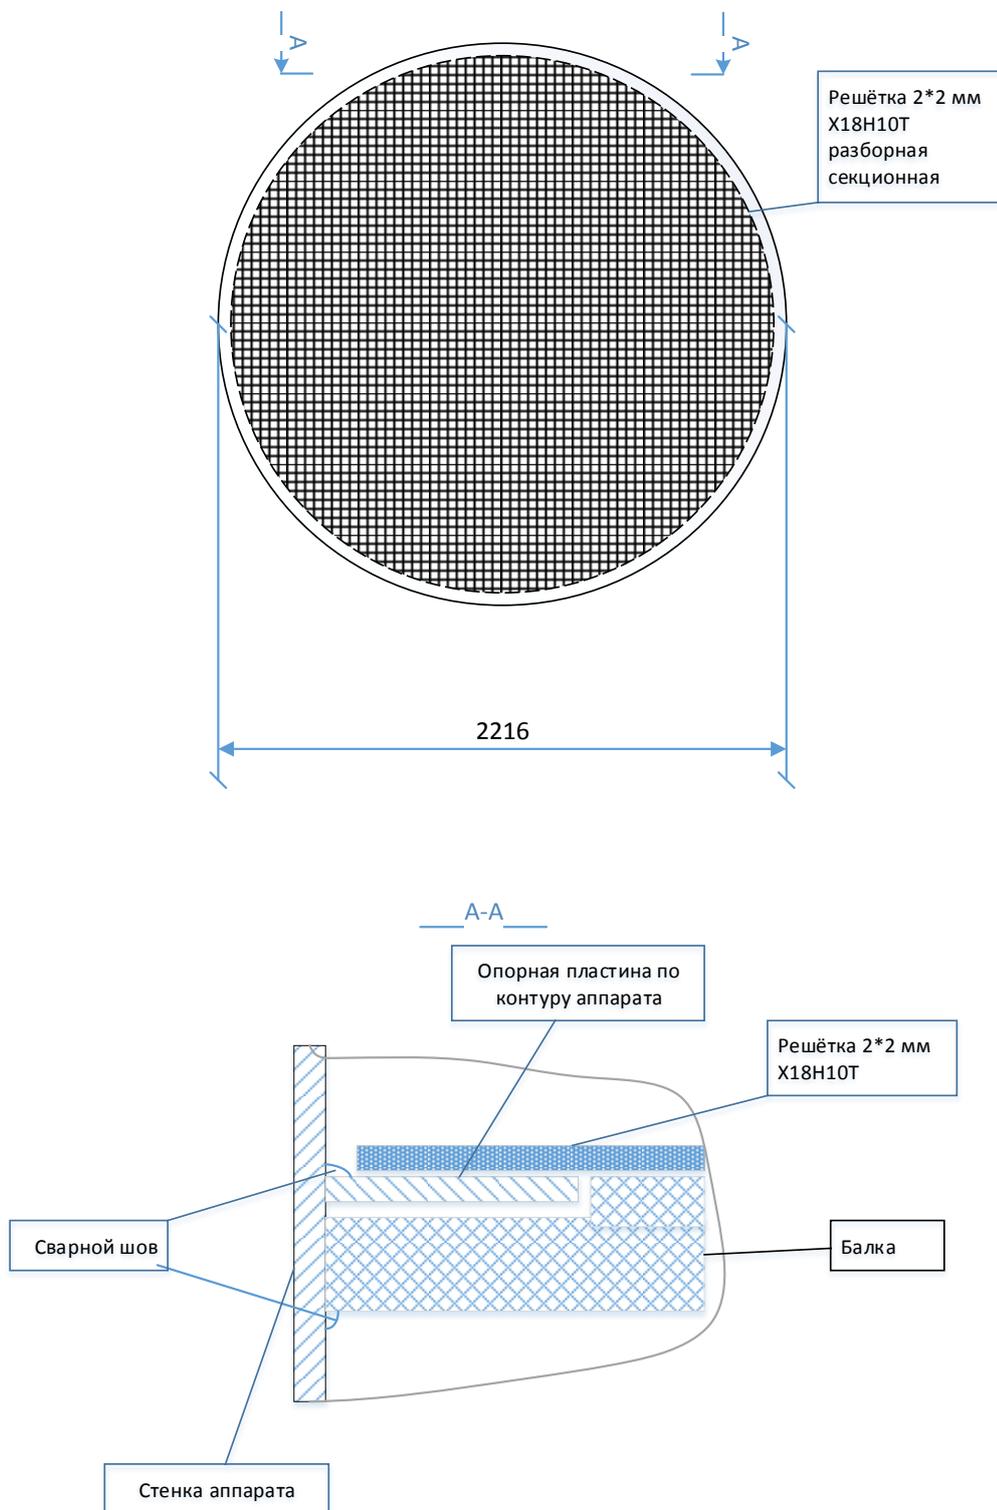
Сборочный чертеж монтажа опорной решетки под катализатор
